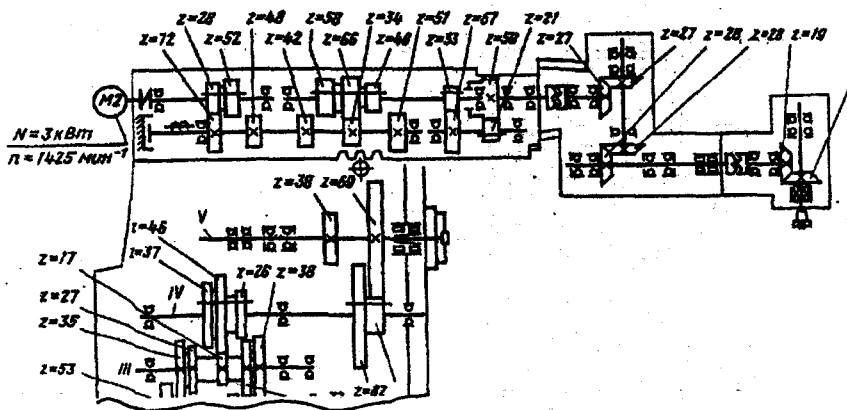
Кінематична схема приводу вертикального шпінделя широкоуніверсального консольно-фрезерного верстата мод. 6Т82Ш-1
